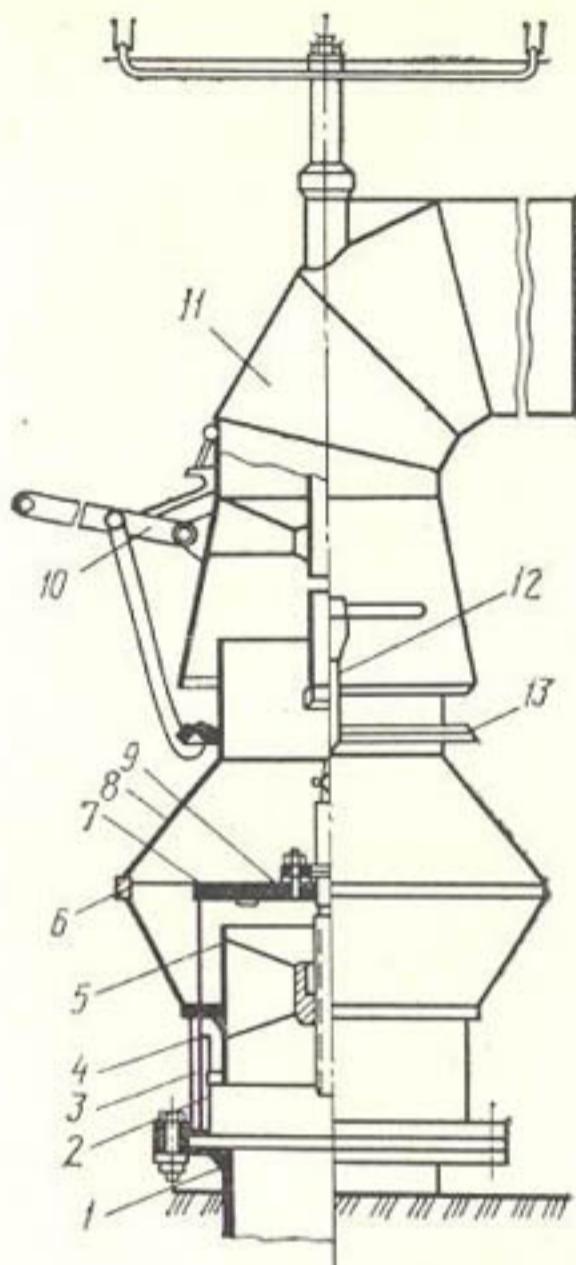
Гидрант-водовыпуск ГВ-3:
